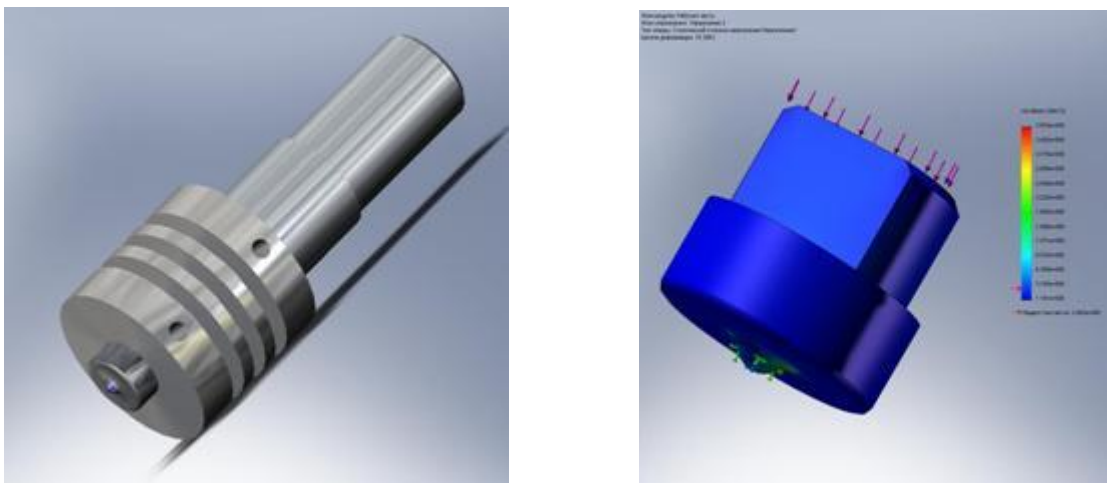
Твёрдотельные модели инструментов для сварки трением, разработанные в системе SolidWorks.
